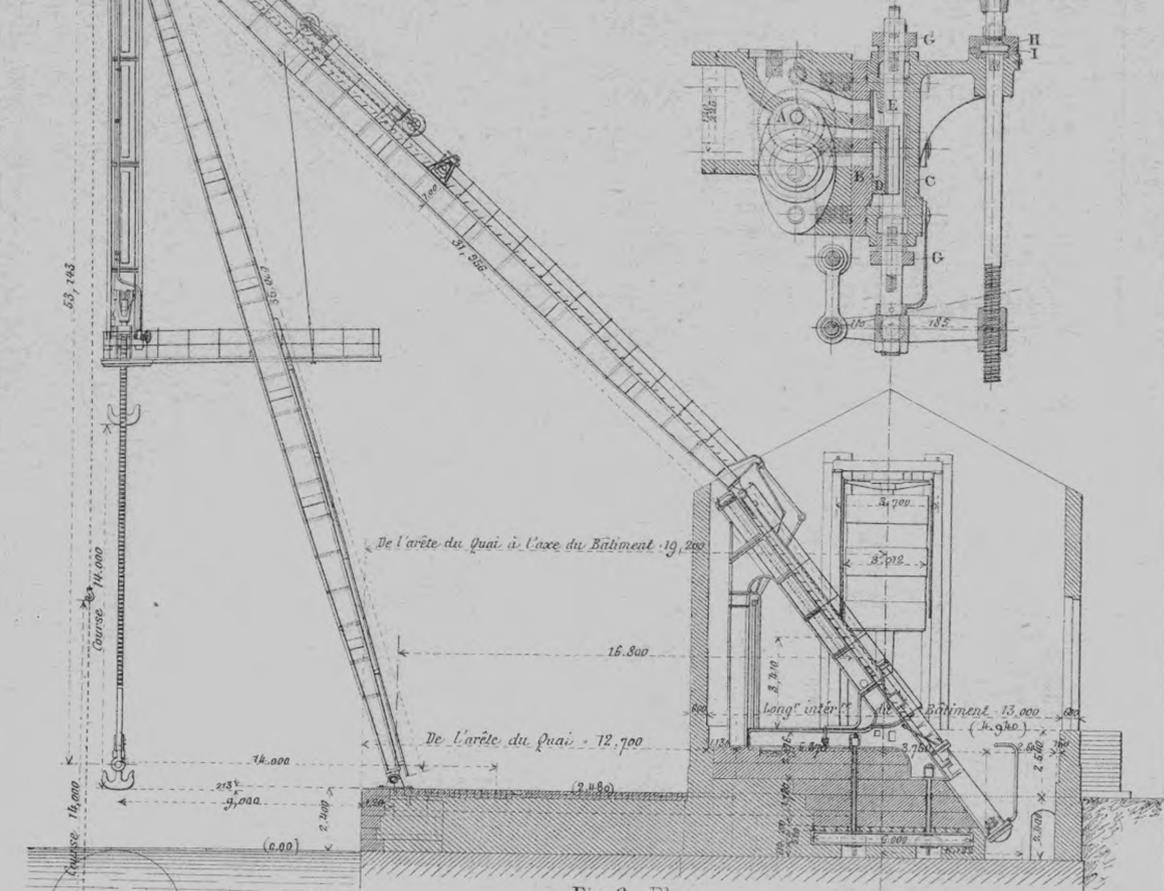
Appareil de distribution du cylindre de levage Coupe verticale
